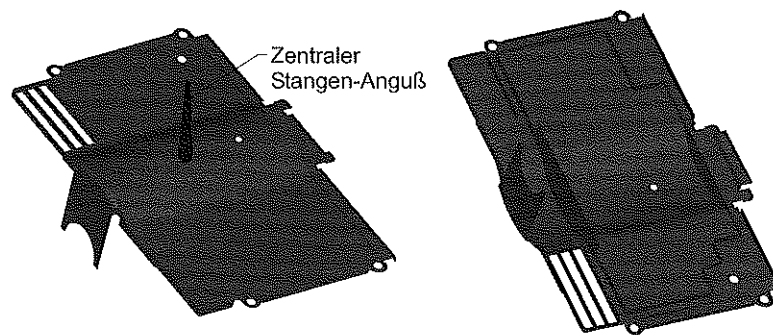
CAD-Modell des für die Voruntersuchungen ausgewählten Spritzgießbauteils in Draufsicht (links) und Rückansicht (rechts).
